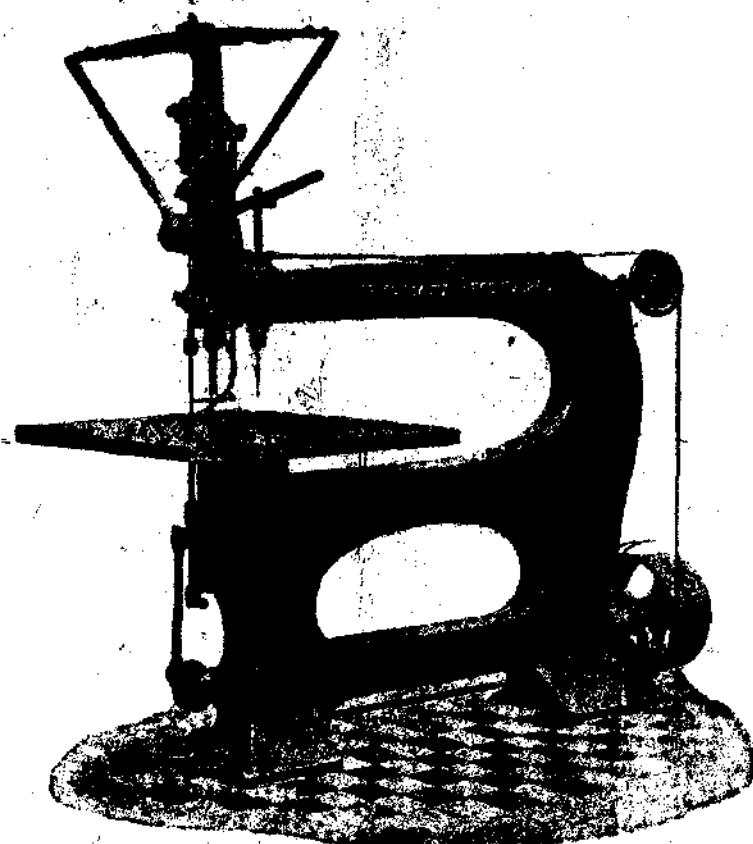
Свободно-стоящий прорезной (ажурный) станок, с скрзными прибором.
